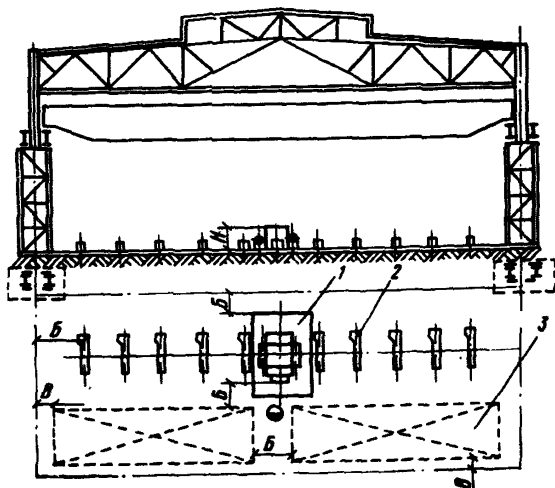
Размещение машины для правки гнбовидности сварных двутавровых балок в поперечном пролете
